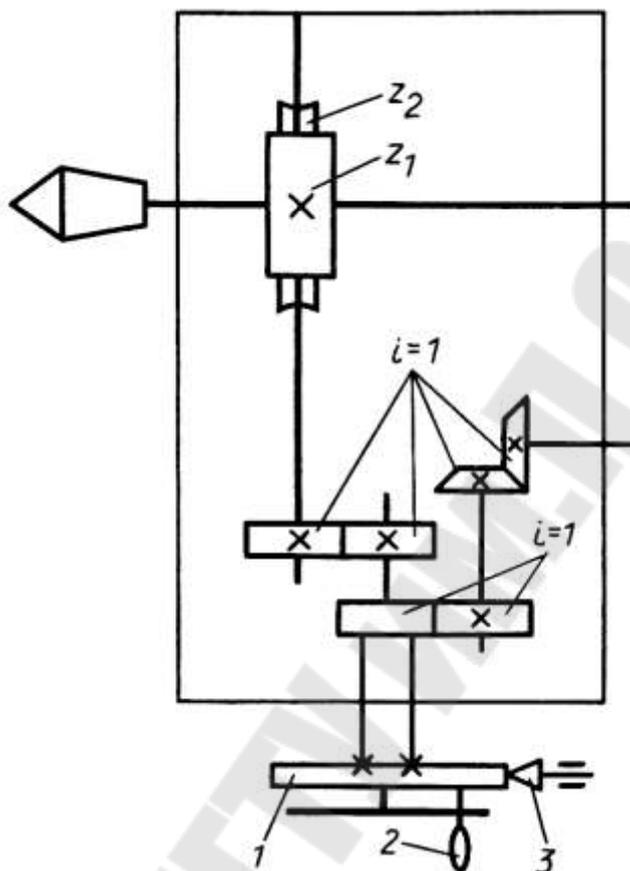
Схема наладки универсальной делительной головки на простое деление
